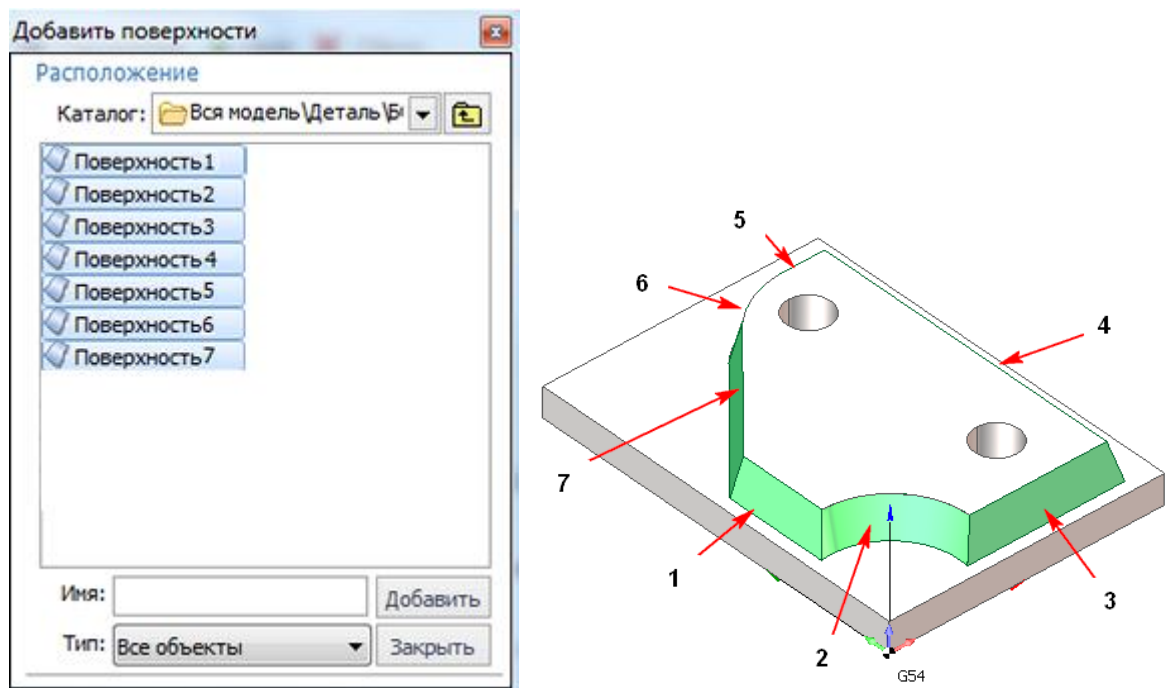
Выбор поверхностей зоны чистовой обработки
